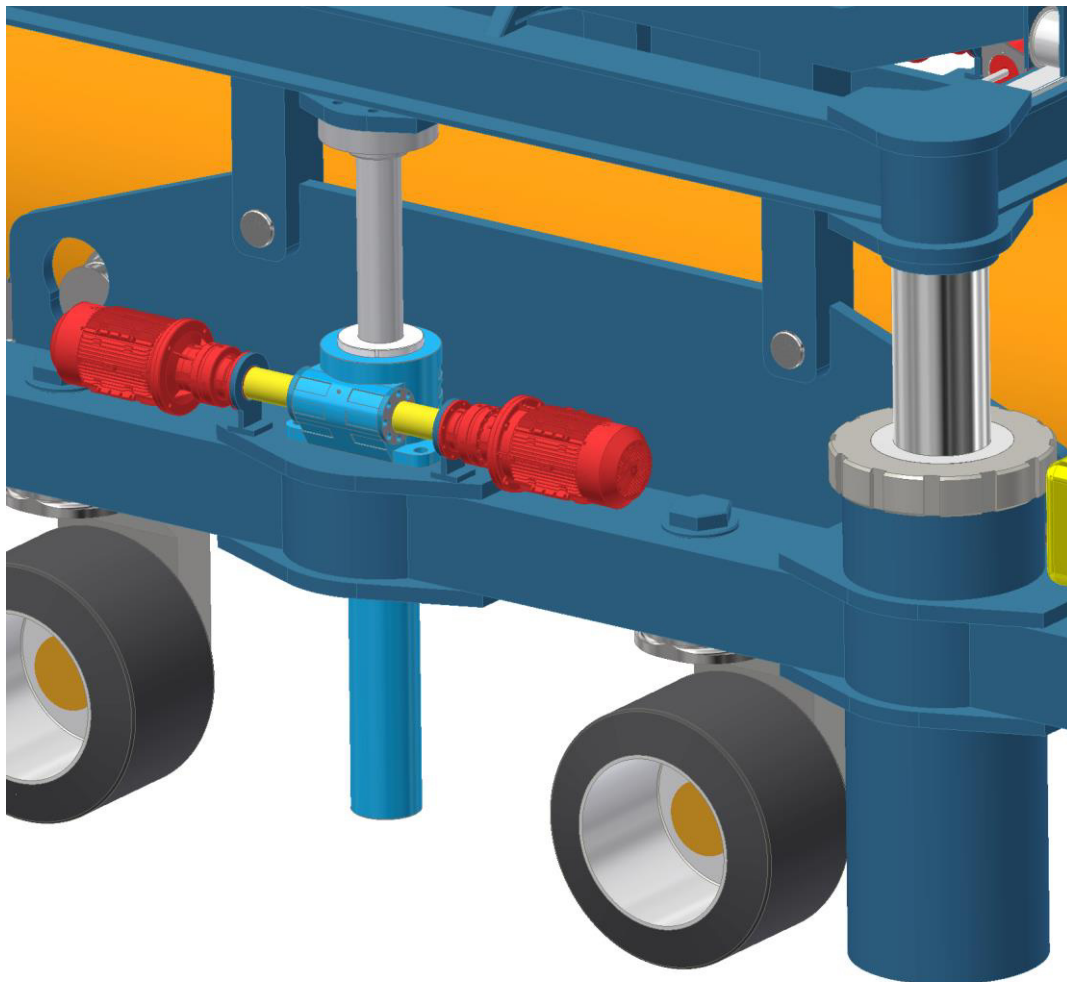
Hubwerk mit redundanten Gewindespindeln
